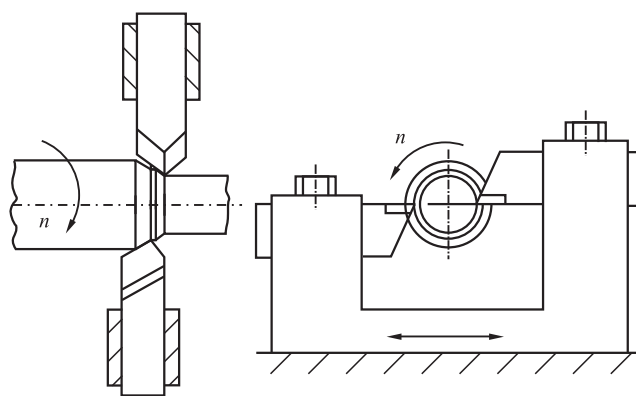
Схема обработки плавающей двухрезцовой головкой
